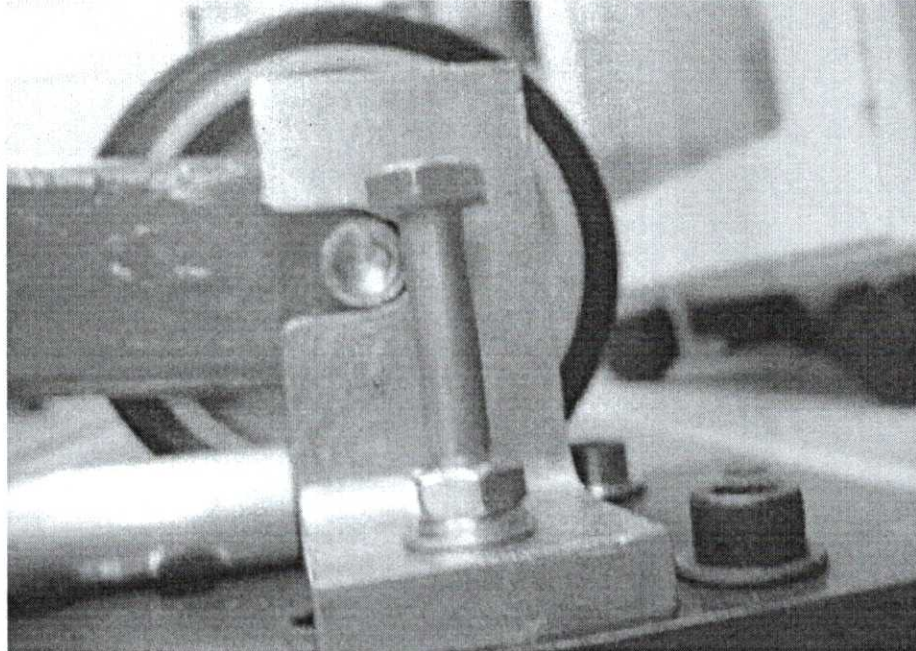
Lado esquerdo da amostra 1 após ensaio.
